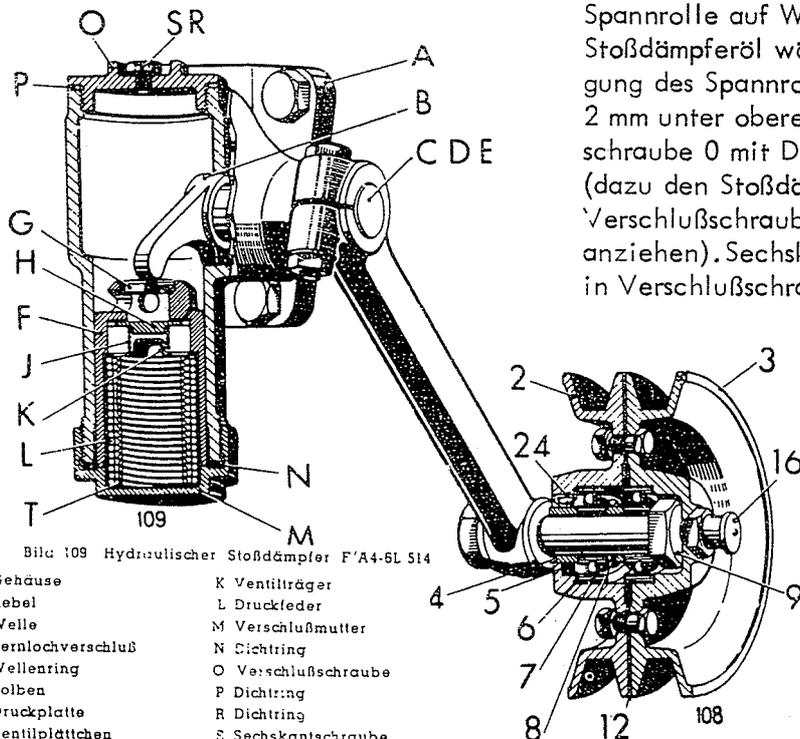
Hydraulischer Stoßdämpfer F/A 4-6L 514
